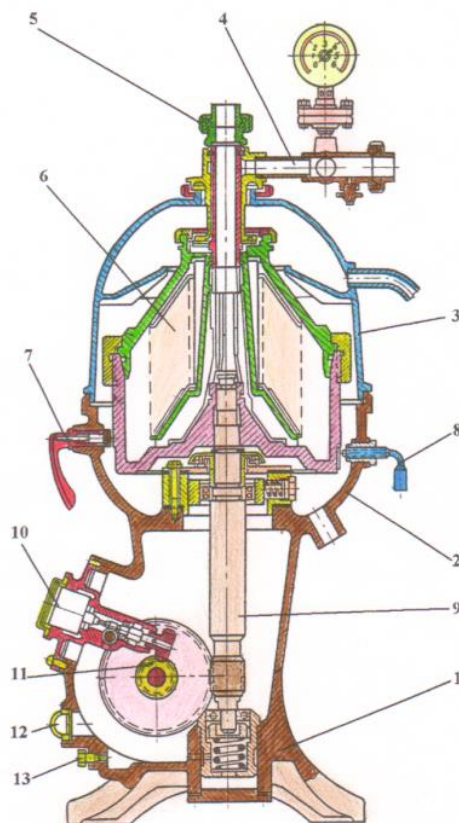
Схема сепаратора молокоочисника: 1 – станина; 2 – чаша; 3 – кришка; 4 – приймально-відвійний пристрій; 5 – гайка-перехідник; 6 – барабан; 7 – гальмо; 8 – стопорний гвинт; 9 – вертикальний вал; 10 – тахометр; 11 – горизонтальний вал; 12 – оглядове скло; 13 – пробка
